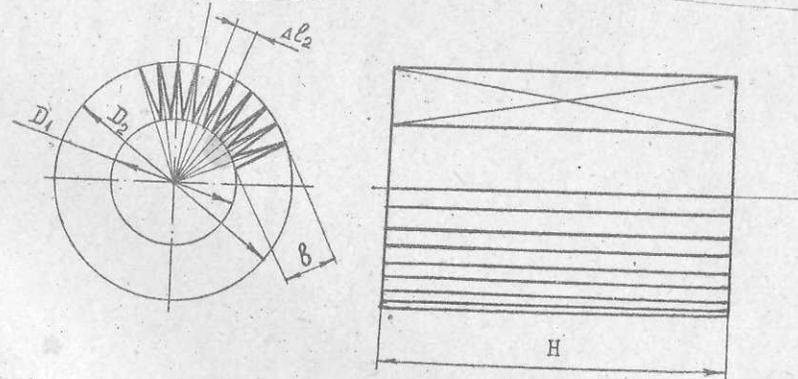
Конструкция фильтровального элемента из проволочных сеток
